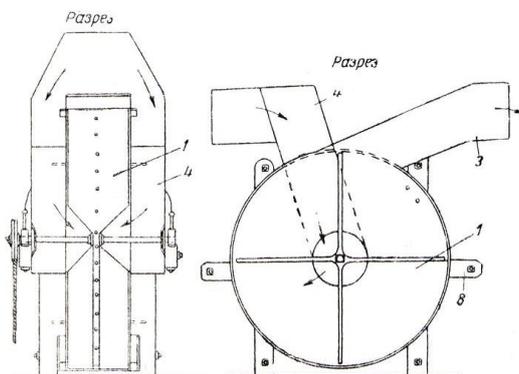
Центробежный вентилятор конструкции Саблукова
